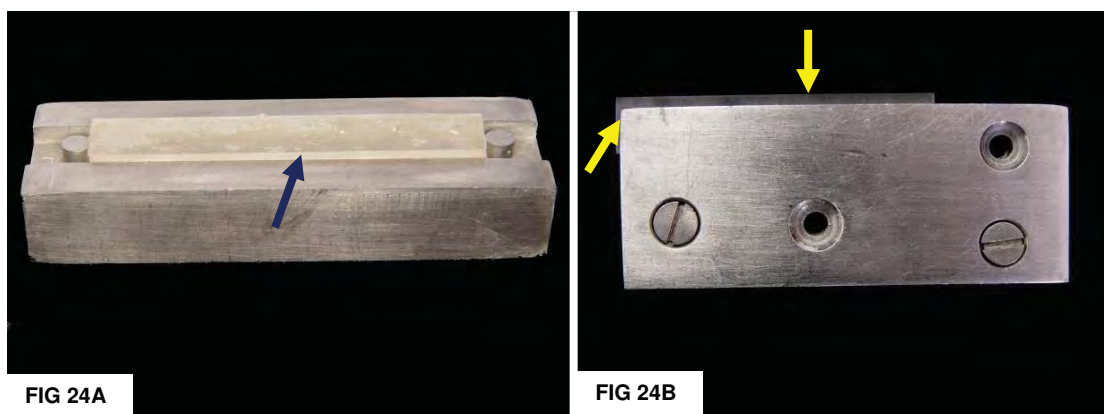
A - Espécime posicionado em matriz metálica, com seta indicando a espessura em excesso. FIGURA 24B - Espécime posicionado em matriz metálica com setas indicando largura e comprimento em excesso.
